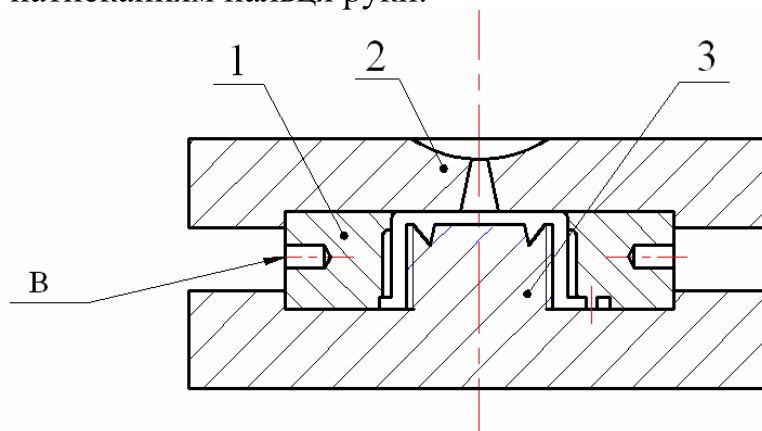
Прес-форма для виготовлення пластмасових заглушок
